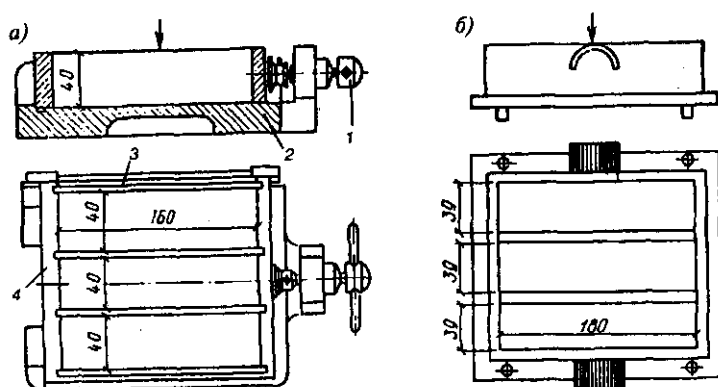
Металлическая разъемная форма для изготовления образцов-балочек (а) и насадка к ней (б)
